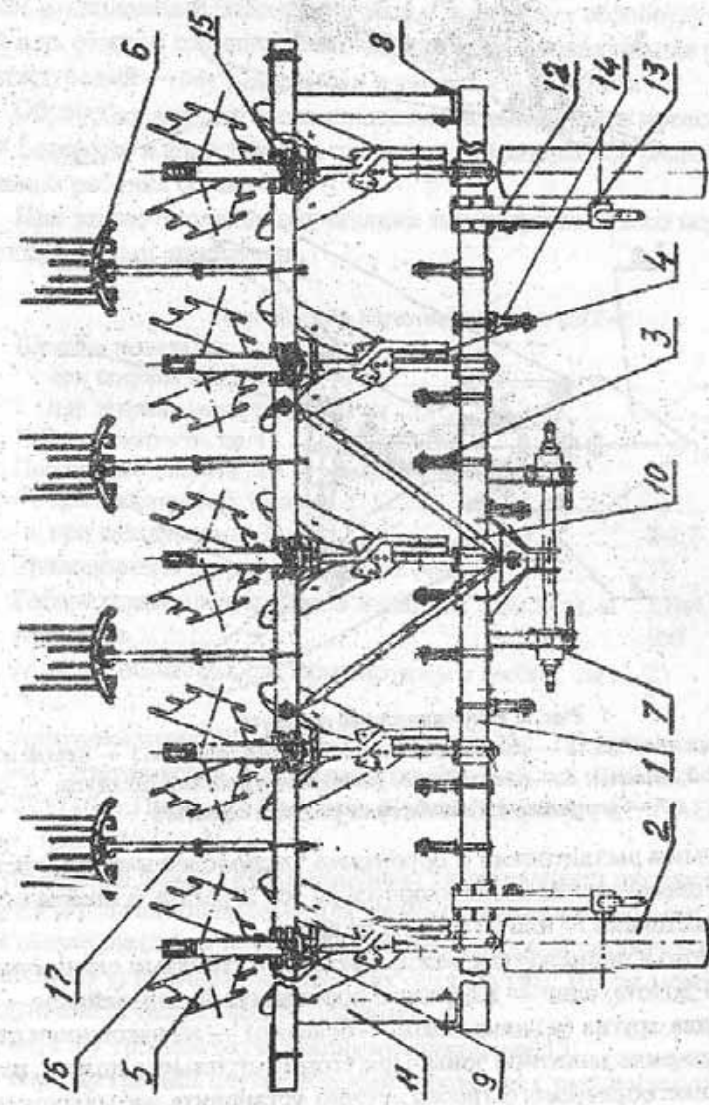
Окучник-культиватор-гребнеобразователь ОКГ-4: 1 — передний брус; 2 — опорное колесо; 3, 14 — кронштейны долот; 4 — с левой окучивающей корпус; 5 — ротационный рыхлитель; 6 — боронок; 7 — автосцепка; 8 — палец; 9 — пружина поводка; 10 — стержень; 11 — задняя рама; 12 — кронштейн; 13 — стойка опорного колеса; 15 — кронштейн поводка; 16 — поводок; 17 — грядиль
